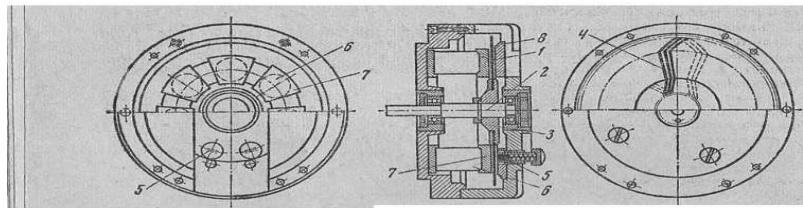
Конструкция двигателя постоянного тока с печатной обмоткой якоря:
